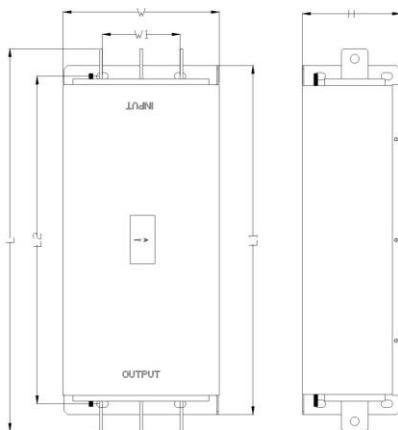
Габаритный чертеж входного волнового фильтра FLT-P04150L-B
